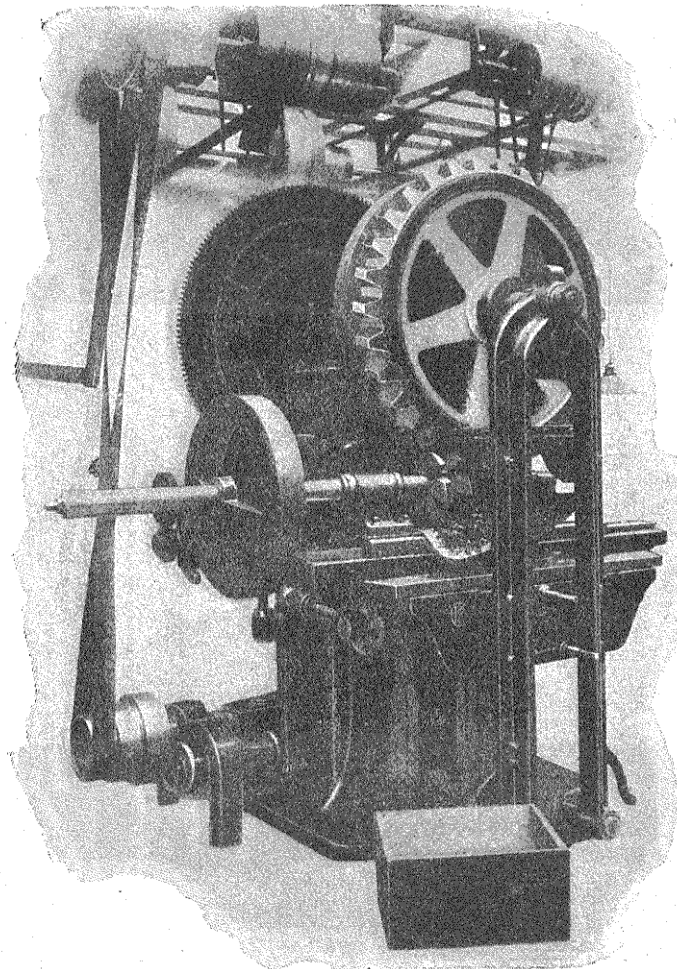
Machine Reinecker à fraiser les roues à vis tangente.
